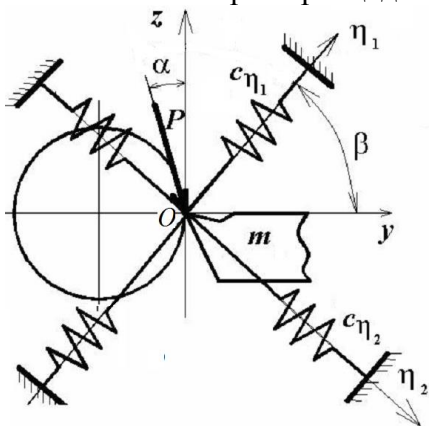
Розрахункова схема пружної системи інструменту токарного верстата в площині yOz
